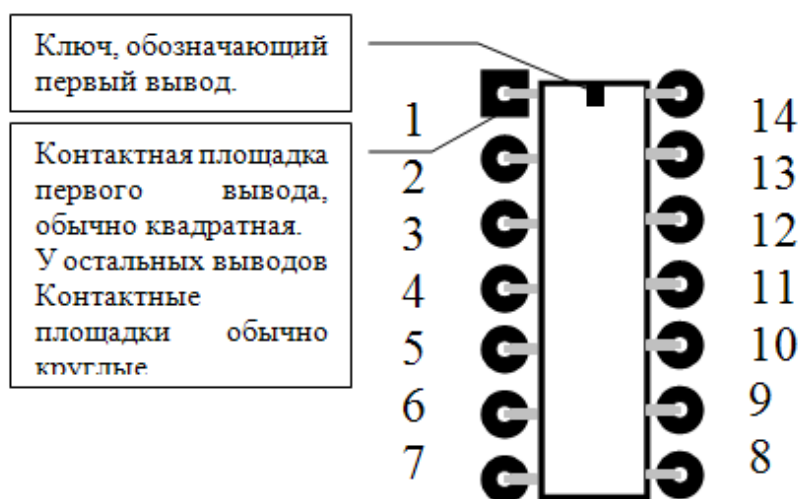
Зовнішній вигляд корпусу DIP -14
